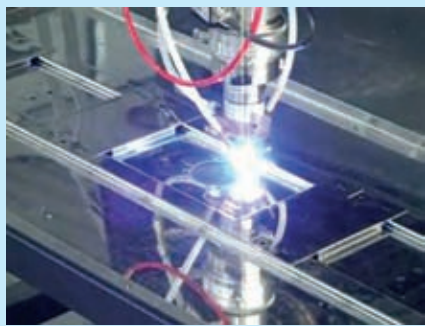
Пятикоординатный лазерный станок для прецизионной резки объемных конструкций
